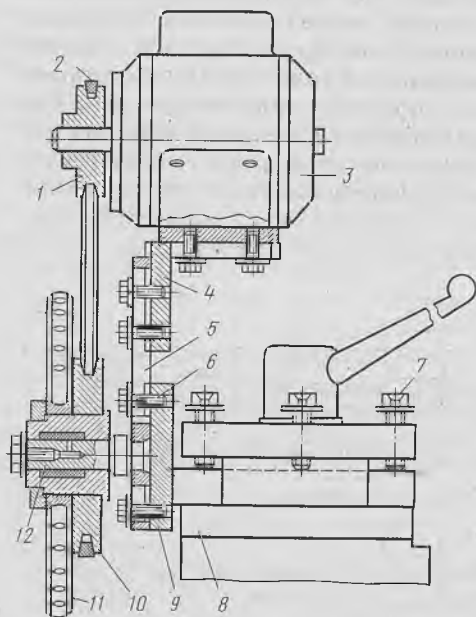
Приспособление для ротационного упрочнения деталей
